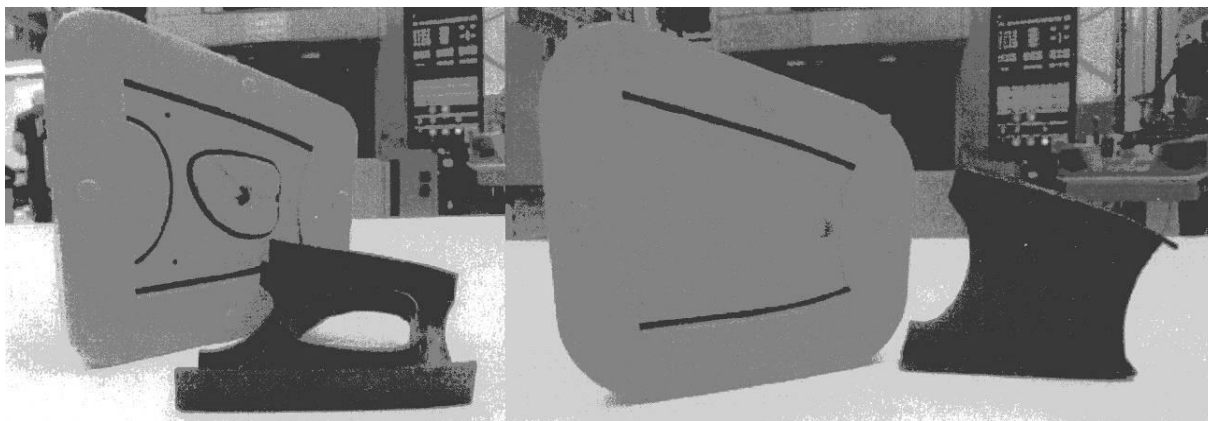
Ребра, изготовленные литьем под давлением (слева) и формованием под давлением (справа)
